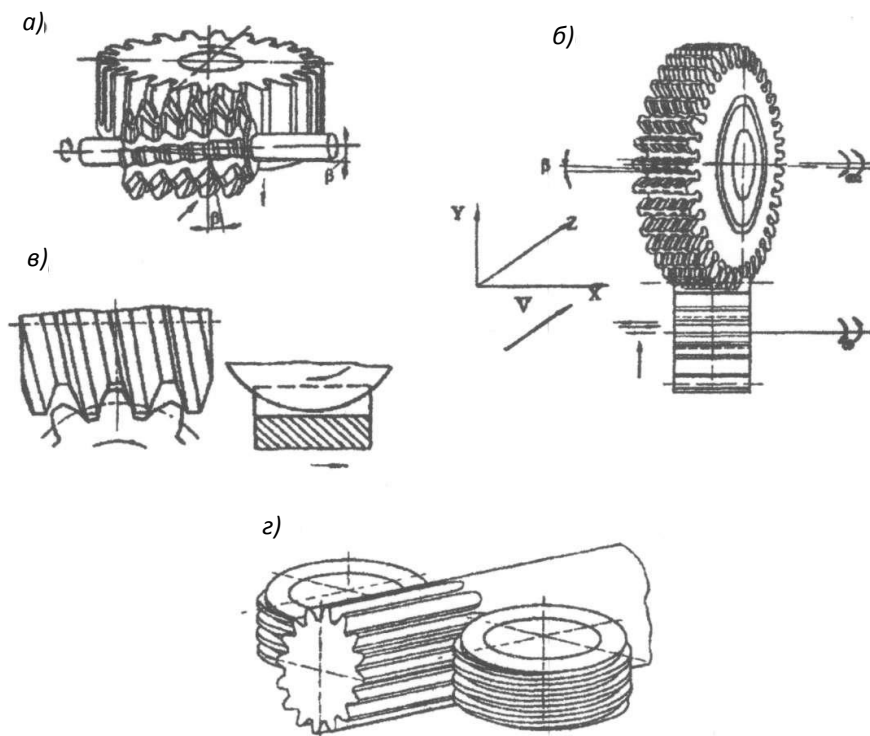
Зубоформуючі інструменти на основі евольвентної гвинтової поверхні
